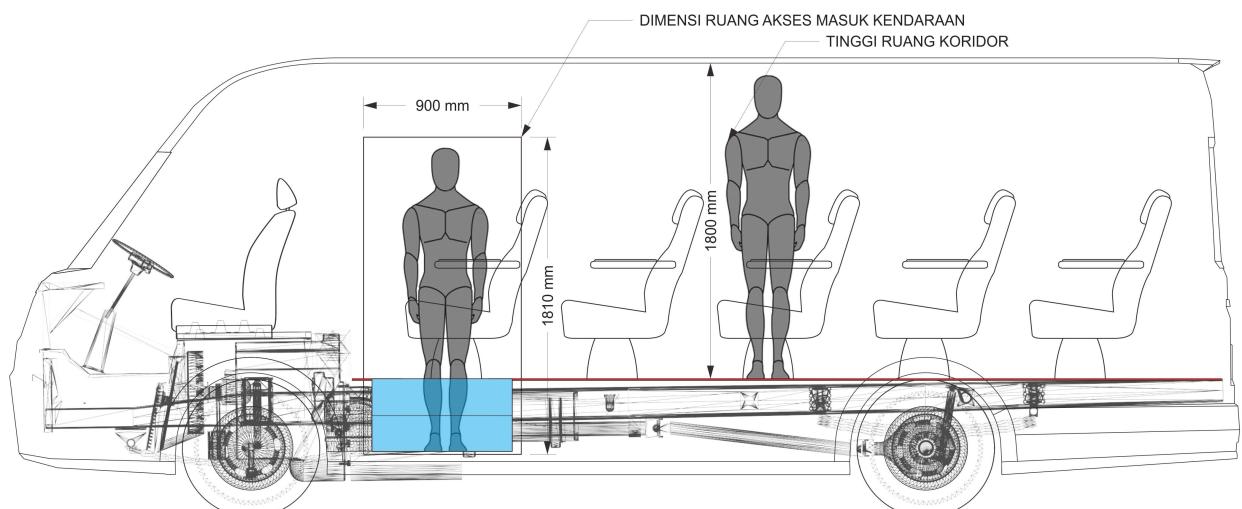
Konfigurasi Passenger Seat Cross Section Depan
